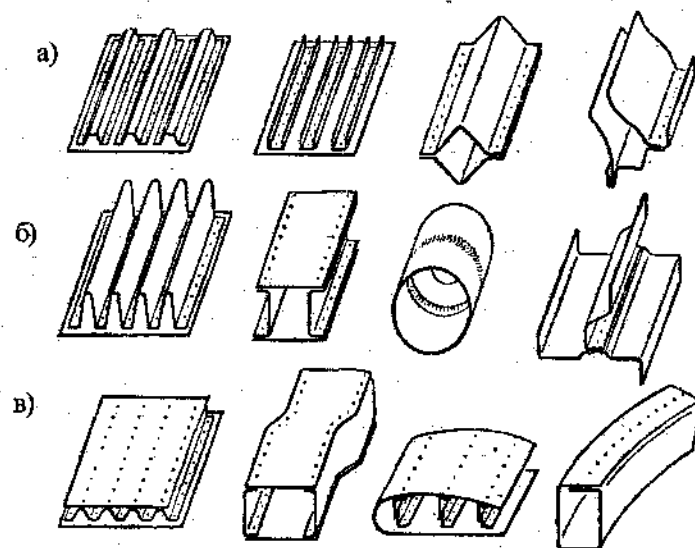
Примеры узлов, соединяемых точечной и шовной сваркой
